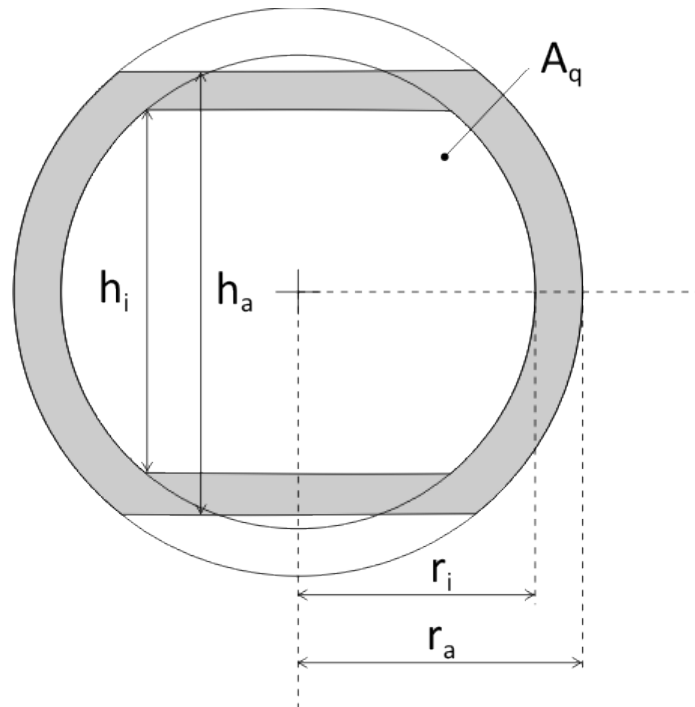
Innenquerschnitt des Schlauchs beim Abquetschen durch die Rollen
